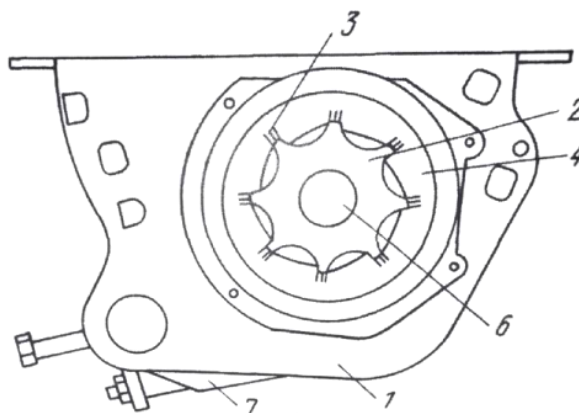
Стандартний котушковий висівний апарат для базової зернової сівалки
